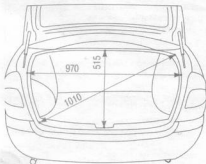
Контрольные размеры проема крышки багажника автомобиля ВАЗ-1118
